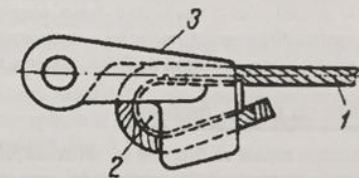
Prinderea în dispozitiv demontabil: 1 - cablu; 2 - piesa de montare a inelului cablului; 3 - piesa de fixare.
